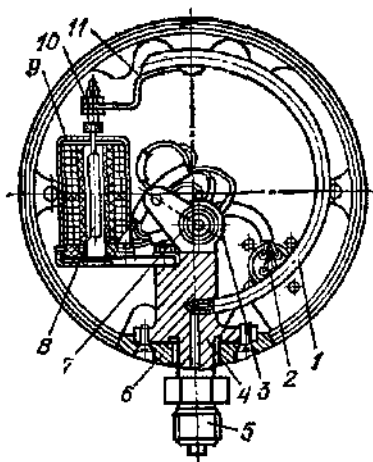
Трубочато-пружинный манометр типа МЭД модели 22364:
